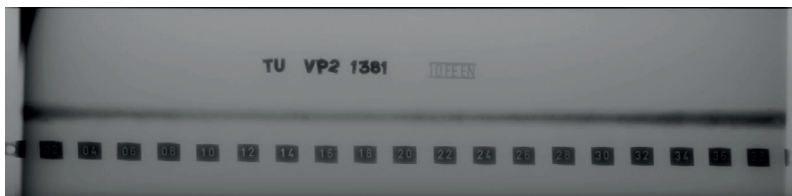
Röntgenfilm einer Schweißung (Lage/Gegenlage-Technik)
